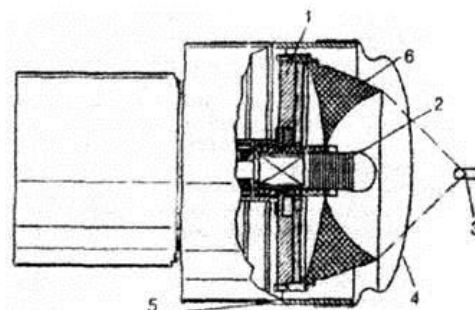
Генеруюча головка (верхній модуль): 1 – перетворювач тиску; 2 – ультразвуковий аплікатор; 3 – фокус; 4 – контактна площа; 5 – корпус головки, 6 – фокус-лінза [3].
